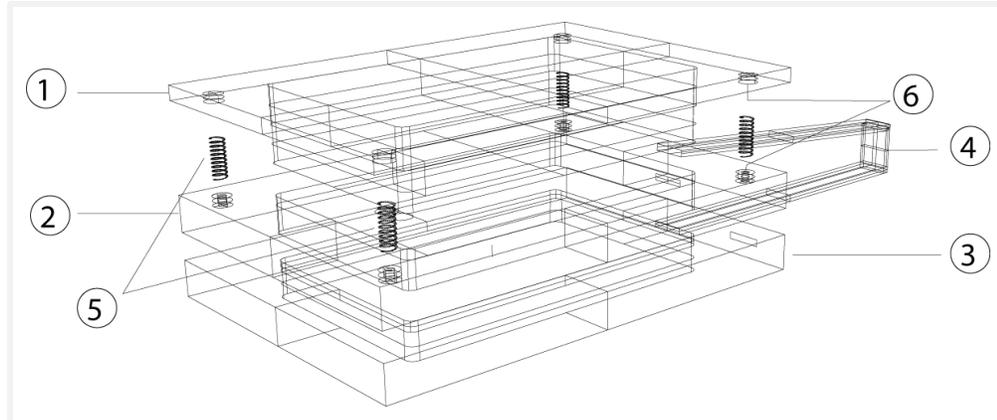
Las partes del troquel de perforado para la pieza #3.
